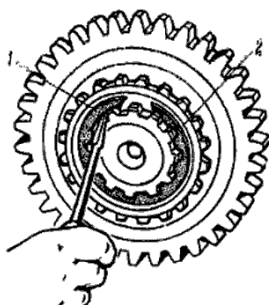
Снятие стопорного кольца ведомой шестерни понижающего редуктора: 1 — стопорное кольцо; 2 — ведомая шестерня
